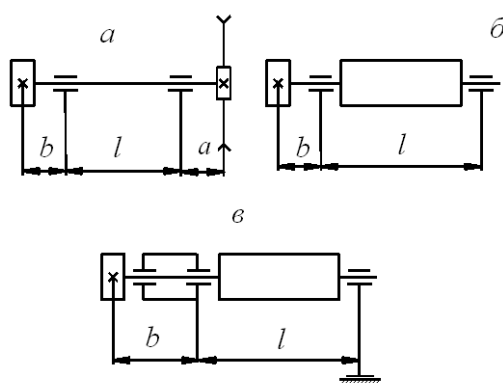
Схемы механизмов главного движения: *a* – шпиндель; *б, в* – ножевой вал
